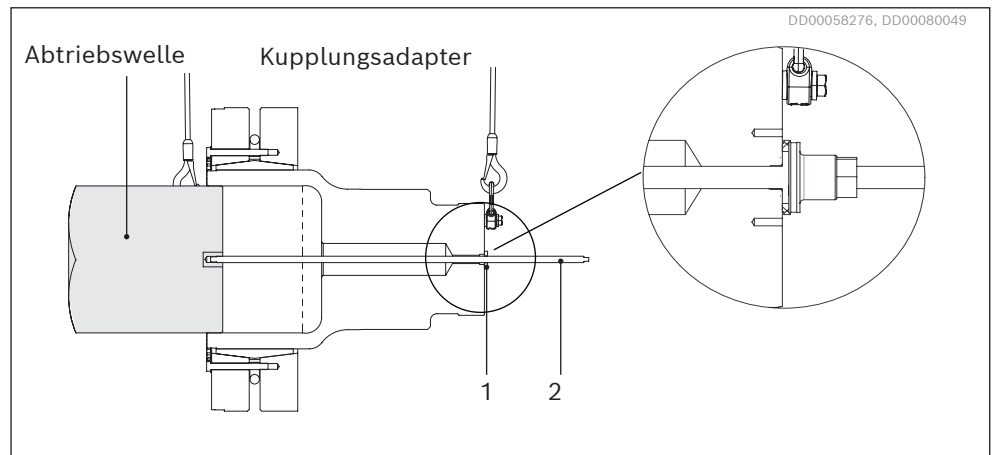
Montage des Kupplungsadapters auf der Abtriebswelle mithilfe des Montagewerkzeuges.
